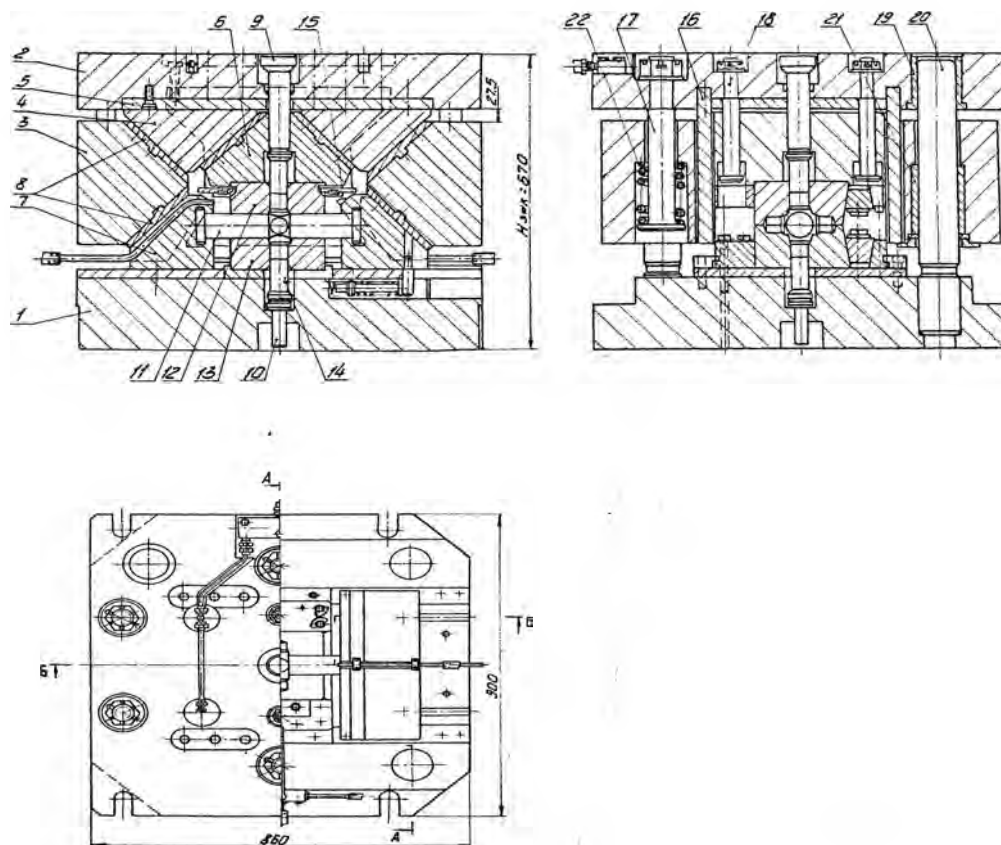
Пакет для безоблойной штамповки крестовины карданного вала
